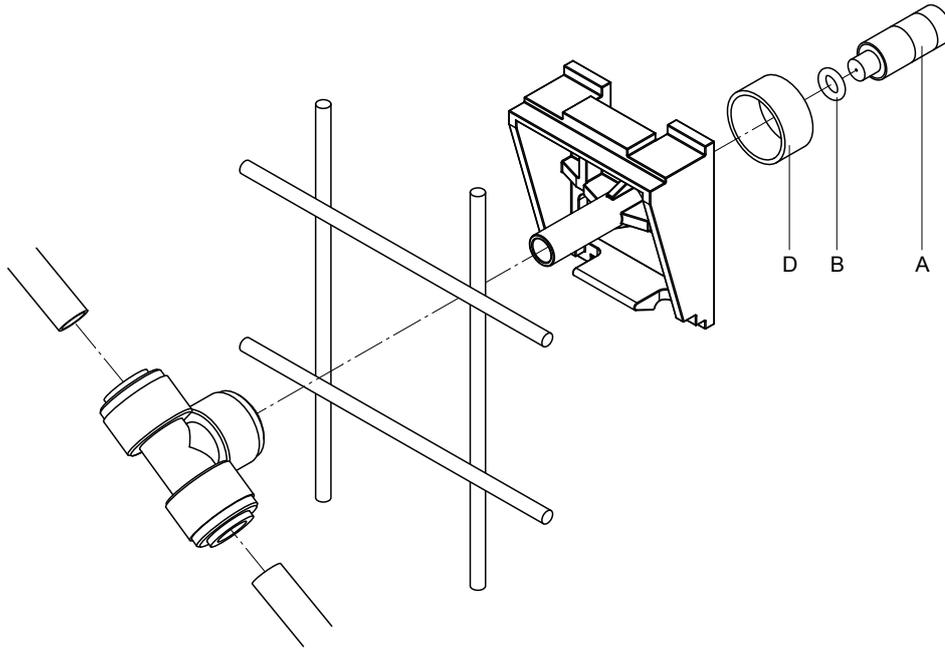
Montaje y desmontaje de los soportes de boquilla
